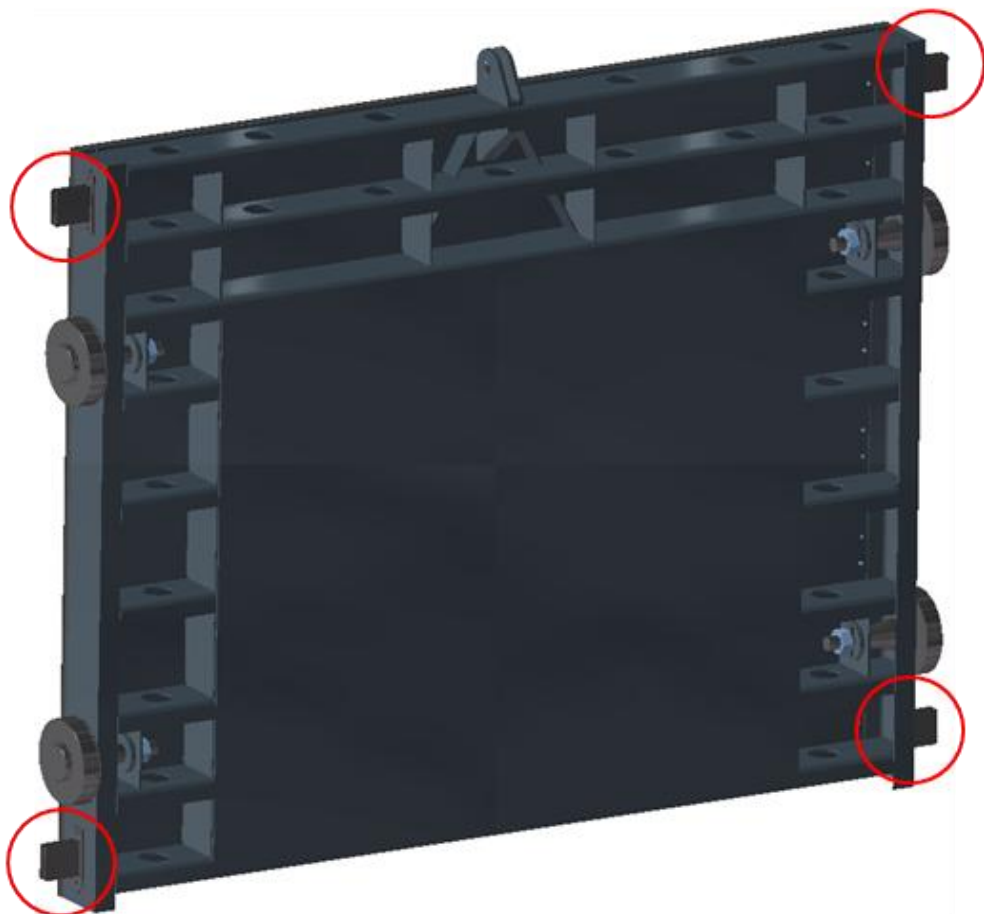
Conjunto sistema de rodillos compuerta mural.
